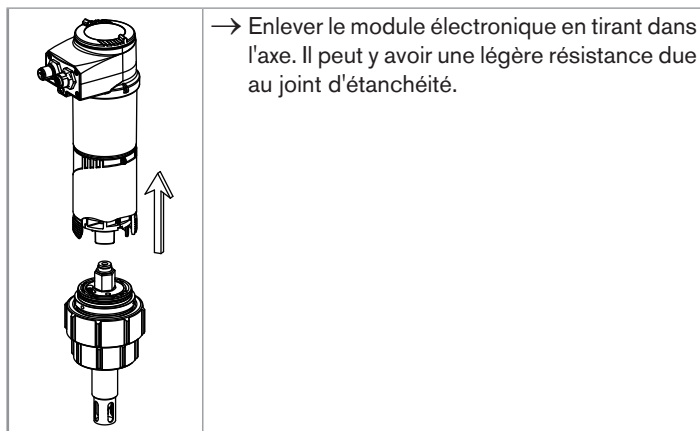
Désassembler le module électronique de l'armature (8202)
